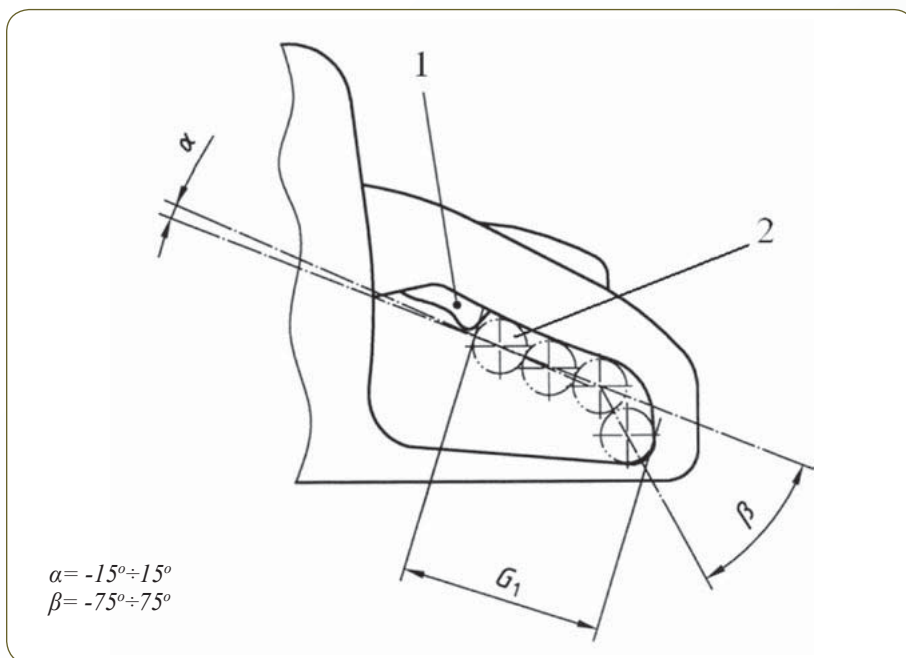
Odstępy i prześwity uchwytu przedniego i uchwytu tylnego pilarek łańcuchowych przenośnych do pielęgnacji drzew
